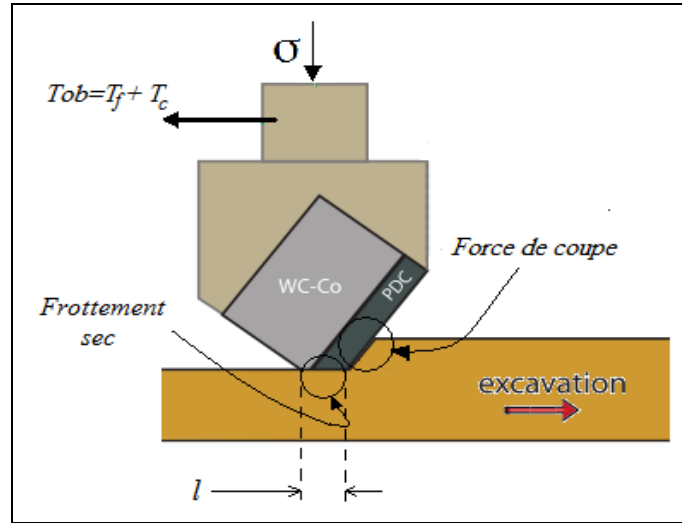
Force de frottement et de coupe sur un élément de coupe
